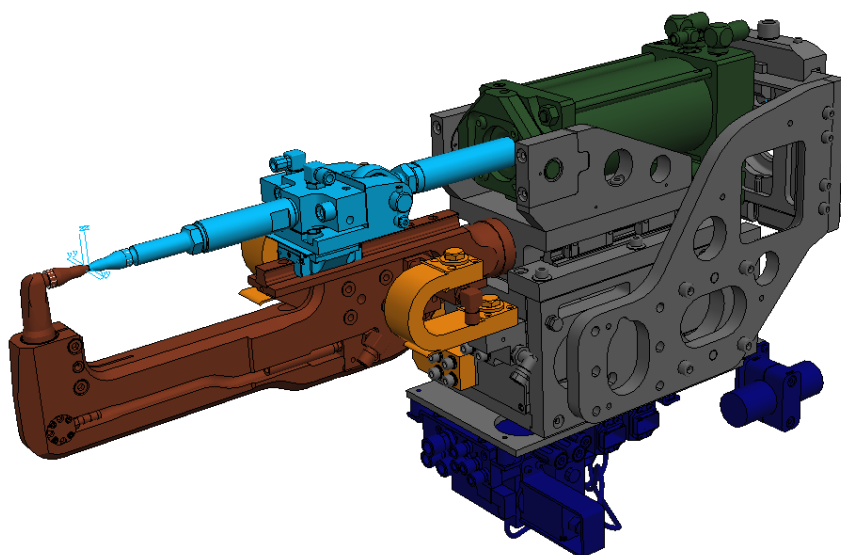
Сварочный пистолет для робота 5080R01 Z
